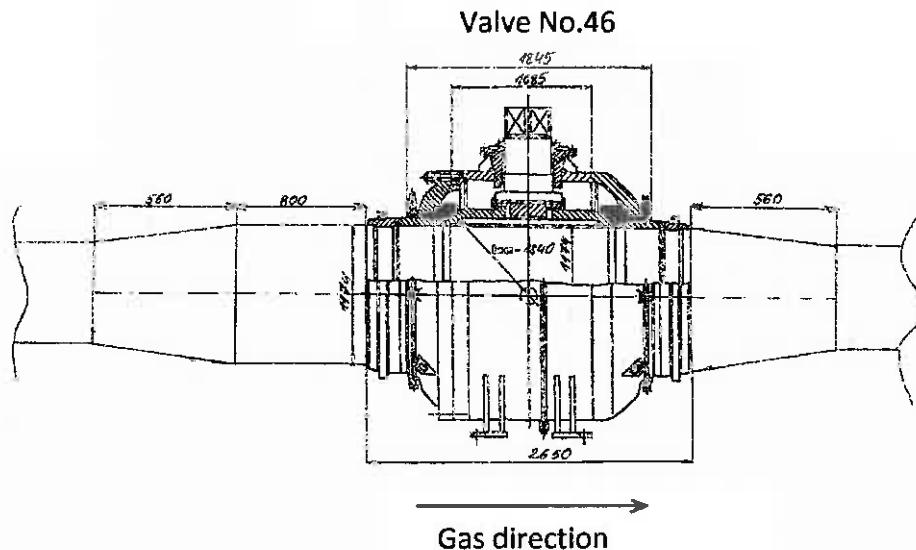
Čiaupo DN 1200 su perėjimais brėžinys / Drawing of valve DN 1200 with reducers
